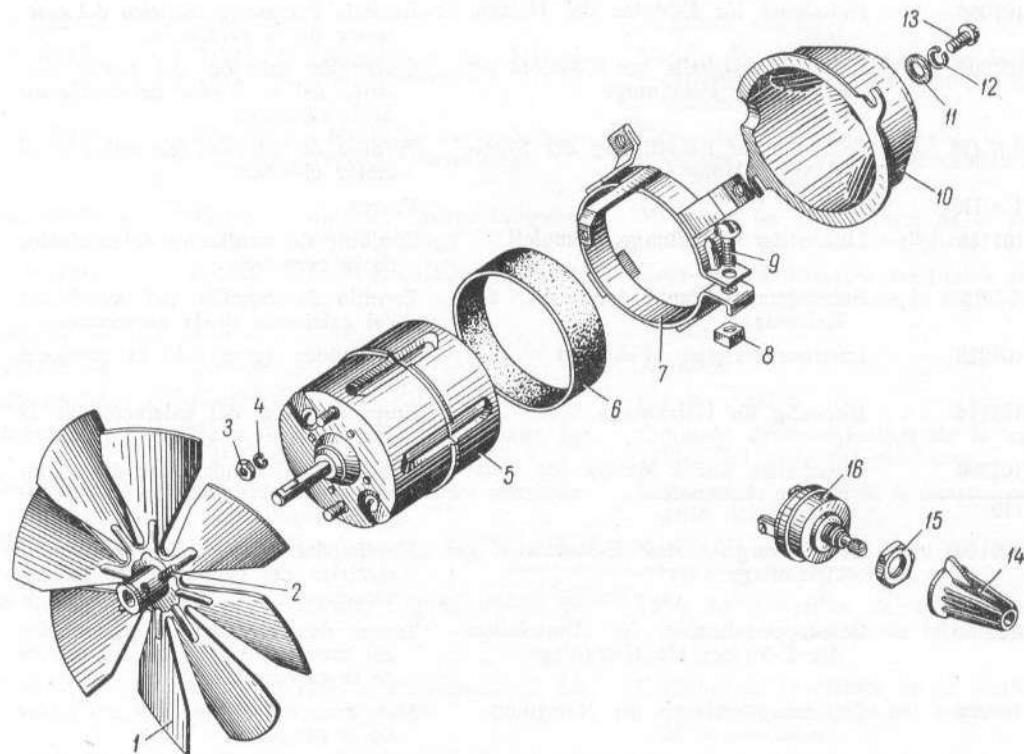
Gebläse mit Motor zu Heizanlage und Windschutzscheibenentfroster
